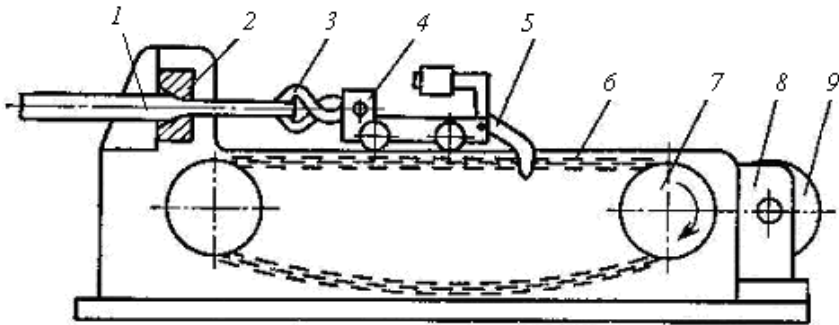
Схема цепного волочильного стана: 1 – заготовка, 2 – волока, 3 – клещи, 4 – волочильная каретка, 5 – крюк, 6 – цепь, 7 – ведущая звездочка, 8 – станина, 9 – электродвигатель
